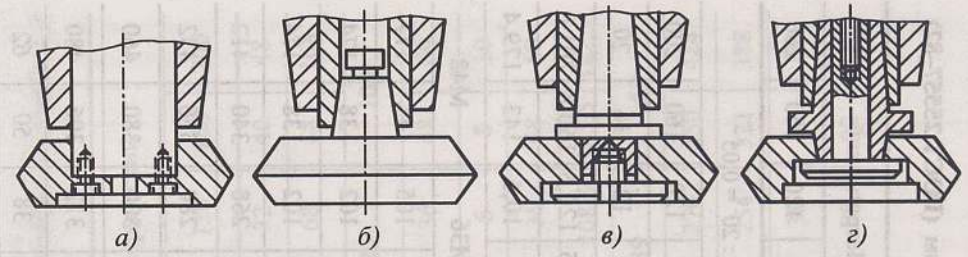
Варианты крепления торцовых фрез на фрезерных станках
